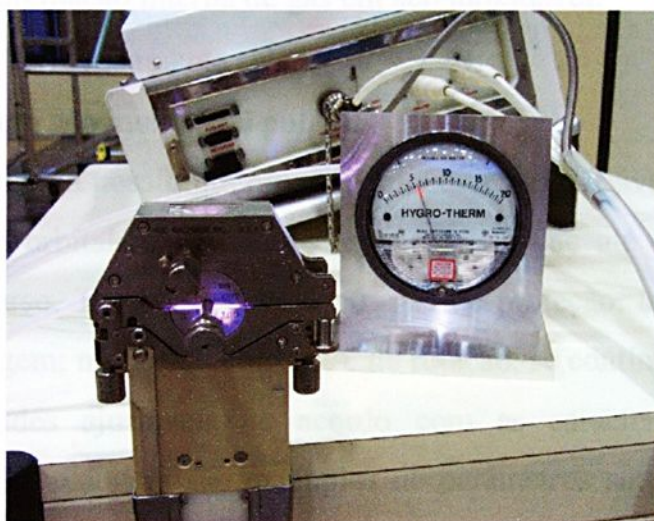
Soldagem TIG orbital dos corpos-de-prova
